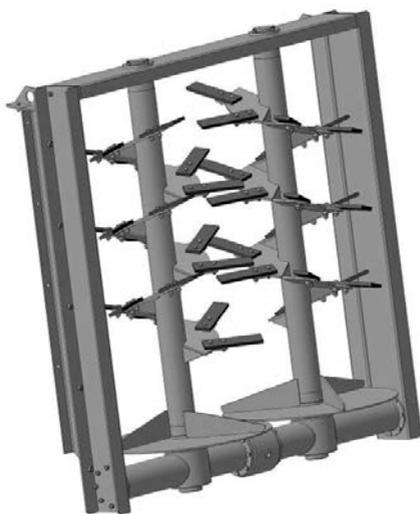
Разбрасывающее устройство с двумя вертикальными барабанами
